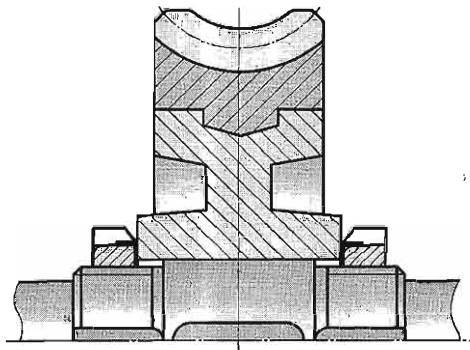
Осевое перемещение червячного колеса по валу с помощью гаек
